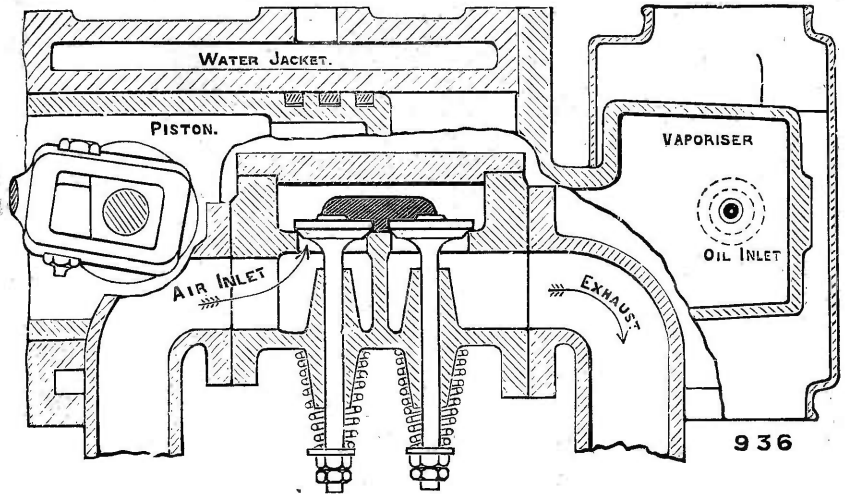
Détail des soupapes du moteur Hornsby-Akroyd.
